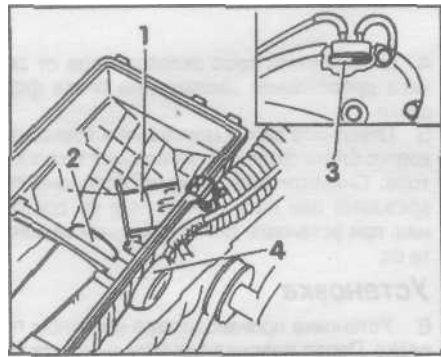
Компоненты подогревателя входного воздуха в корпусе воздухоочистителя
